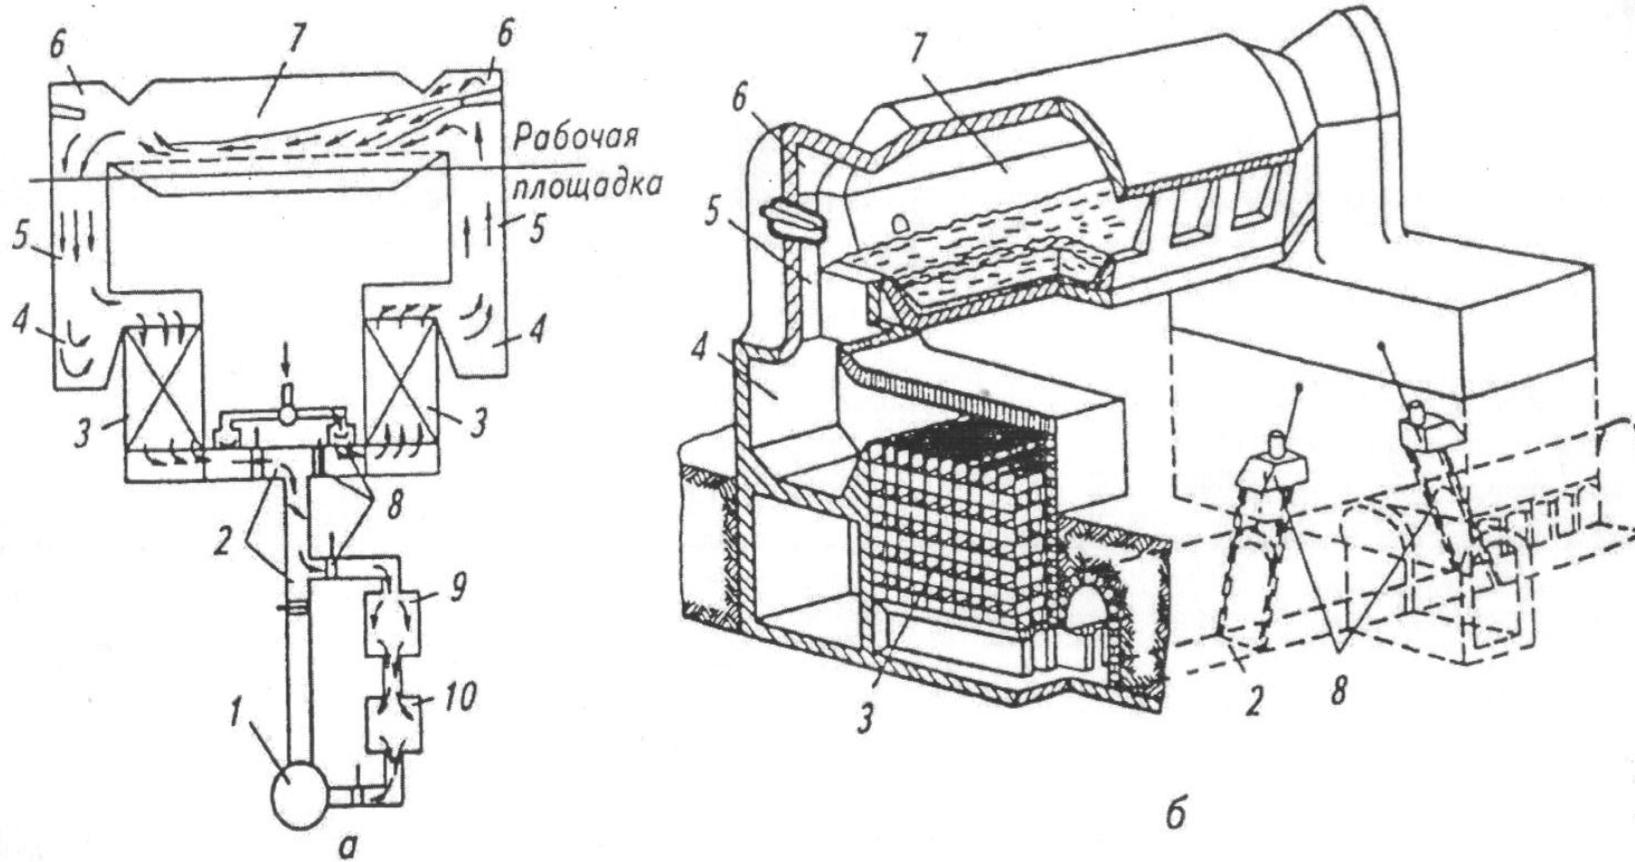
Схема устройства (а) и общий вид (б) маргеновской печи: 1 - дымовая труба; 2 - боров; 3 - регенератор; 4 - шлаковик; 5 - вертикальный канал; 6 - головка; 7 рабочее пространство; 8 - реверсные и регулирующие клапаны; 9 - котел-утилизатор; 10 -газоочистка.
